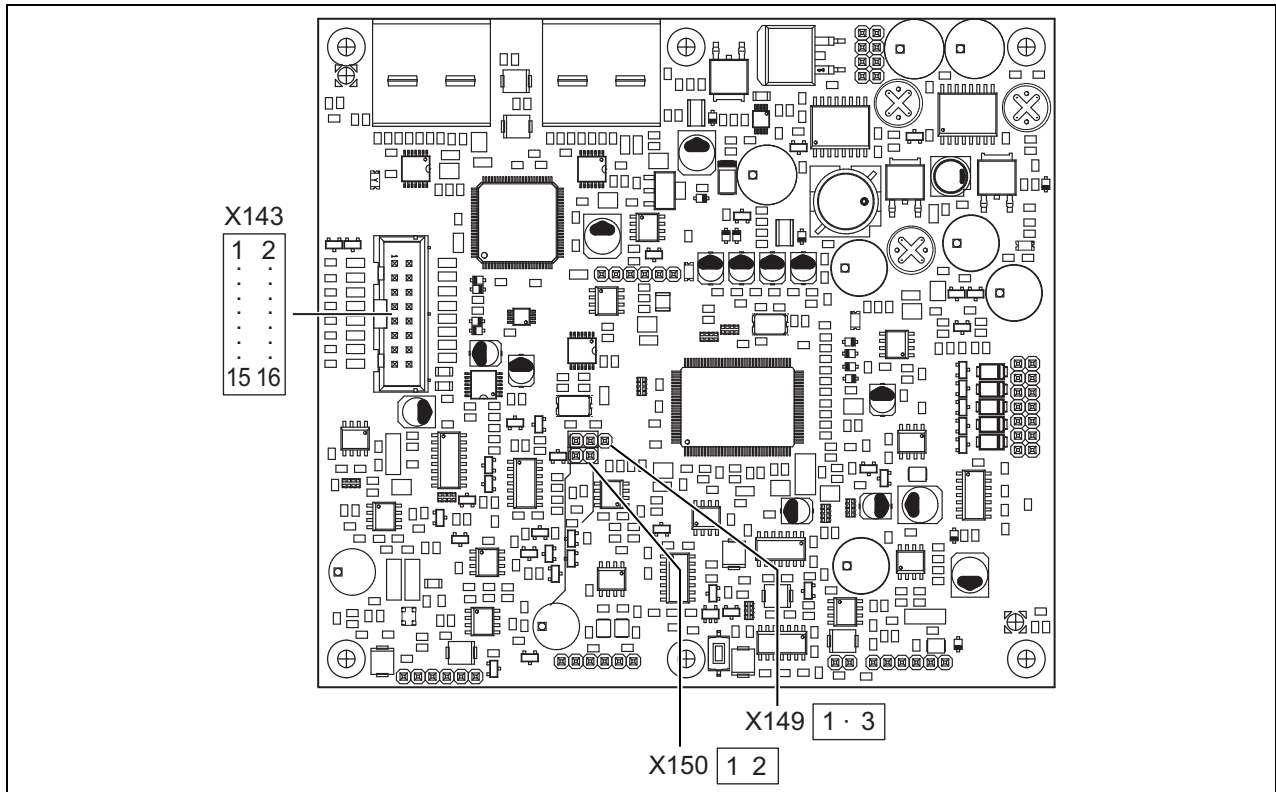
PRS-CSM 의 구성부품 측면 PCB
